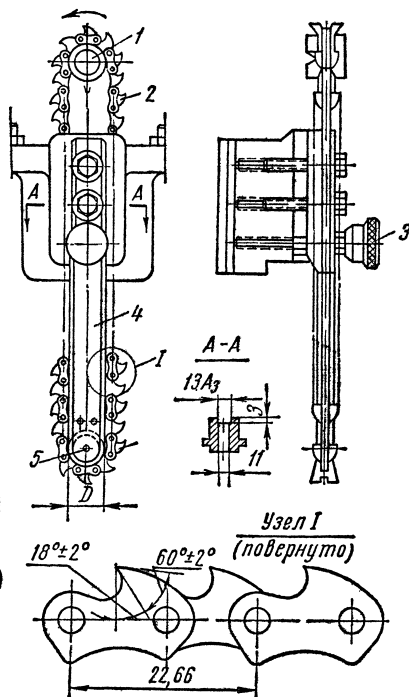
Направляющая линейка с цепочкой цепнодолбежного станка:
